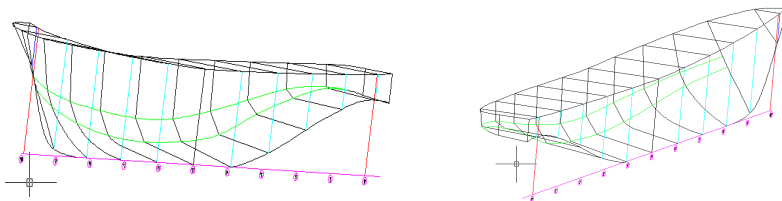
3D-модель наружной обшивки в AutoCAD.
